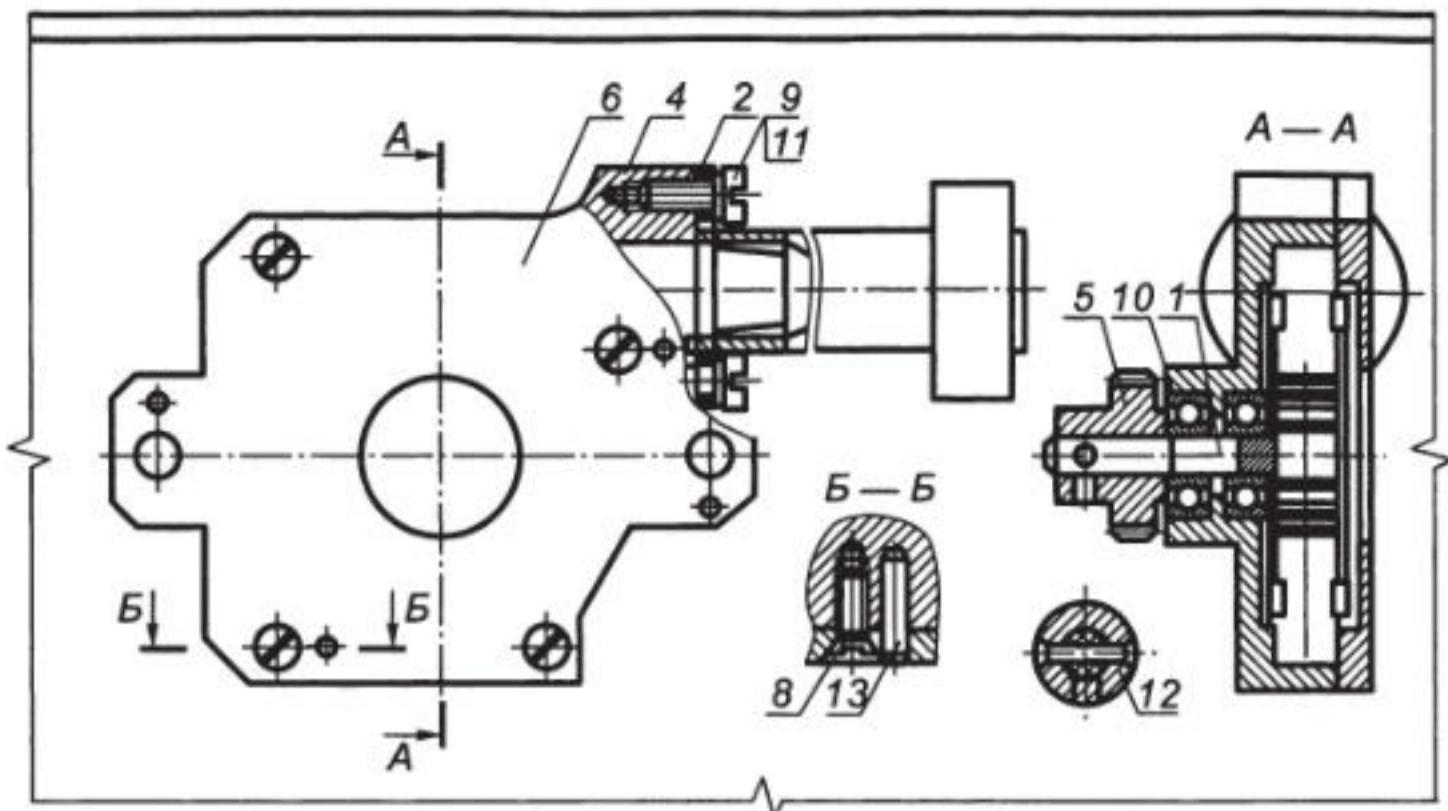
Сборочный чертеж вентилятора, общий вид которого приведен на рис. 9.5
